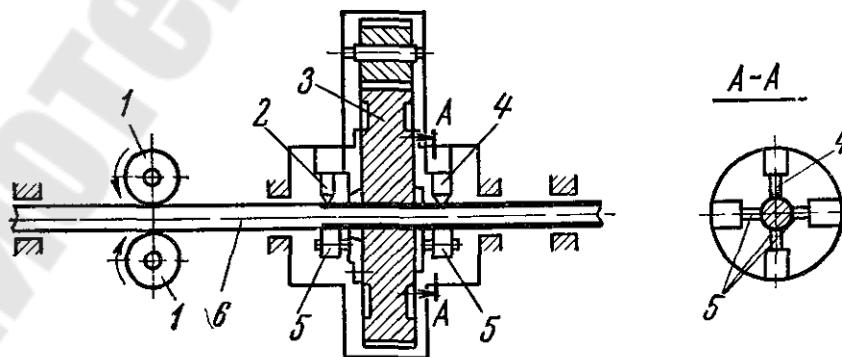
Схема бесцентрово-обдирочного станка
